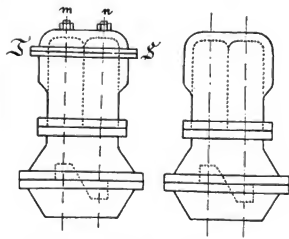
³²⁾ Ältere Konstruktion mit Uebelstand zum Entfernen des Kesselsteins.
